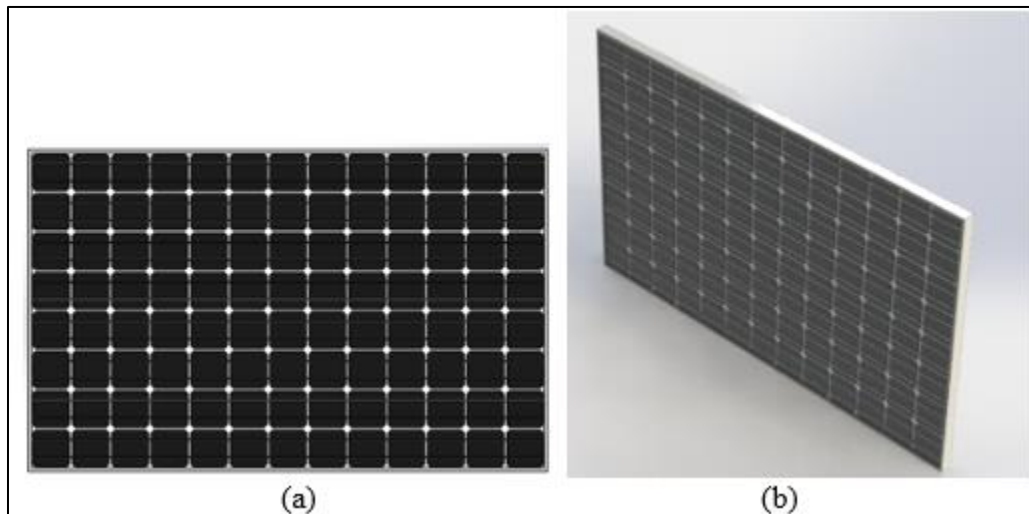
Panel modelado en SolidWorks. (a) Vista en alzado, (b) Renderizado
